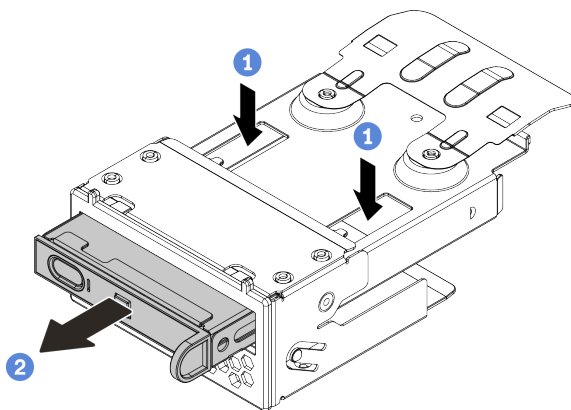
Remoção do conjunto do painel de diagnóstico integrado
